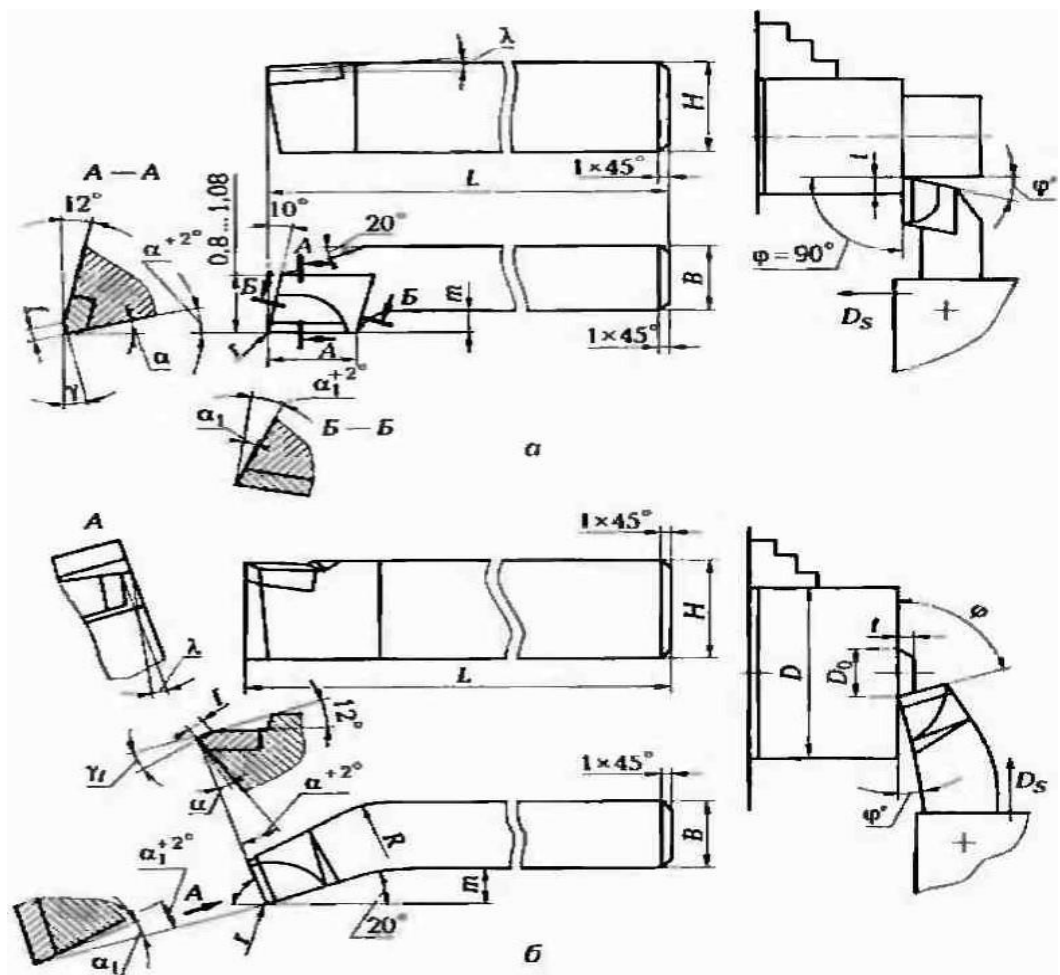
Токарные резцы, оснащенные пластинами из твердого сплава:
